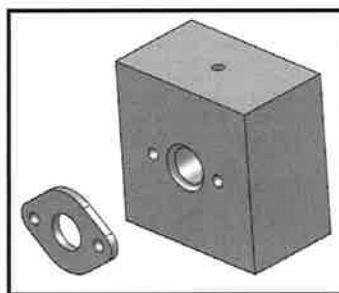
Placa retén para O-ring de sujeción de tubo.
